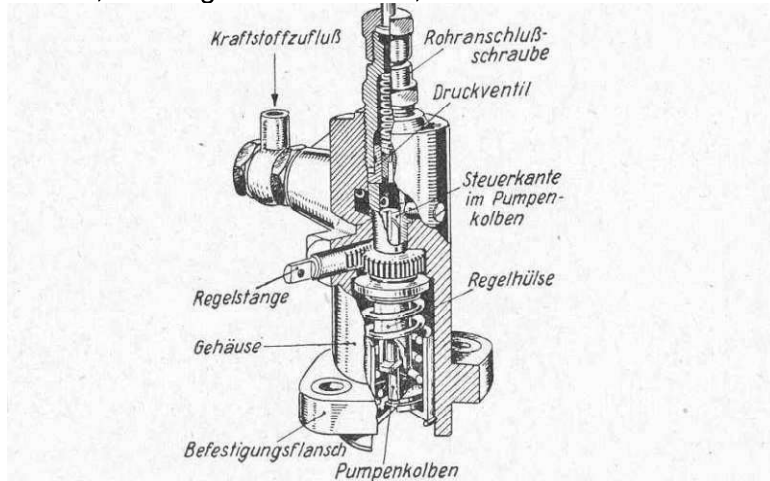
BOSCH – PF – Einspritzpumpe mit Fremdantrieb
